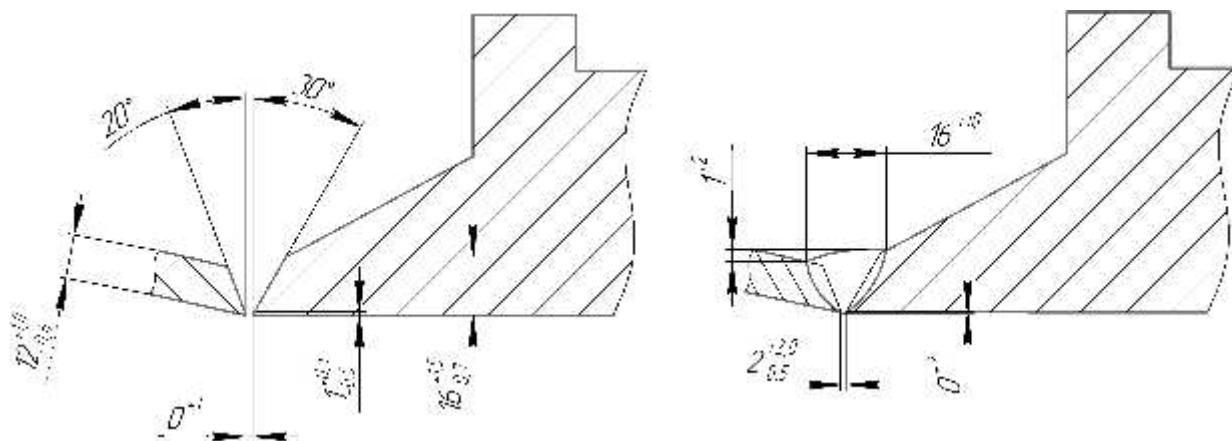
"Разделка кромок под сварку"
